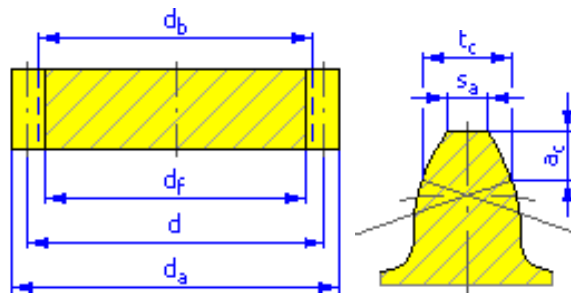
Профиль зуба и зубчатого колеса, шестерни
